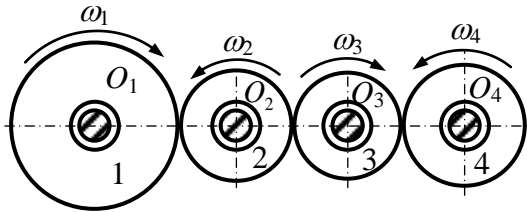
Схема рядового з’єднання зубчастих коліс з паразитними колесами
